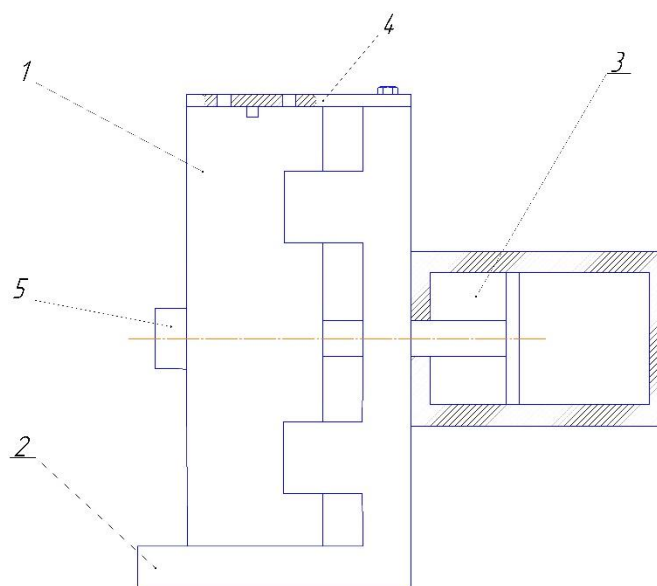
Кинематическая схема пневматического зажима с кондуктором
